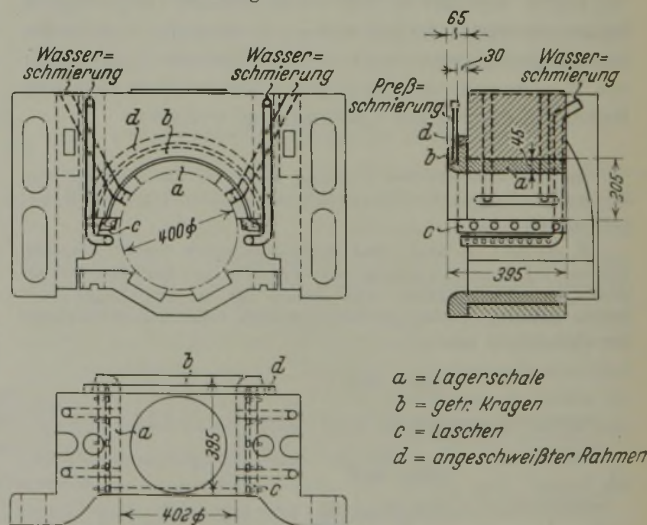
Oberer Einbau zur 750er Trägerstraße mit Kunstharzlagern.
